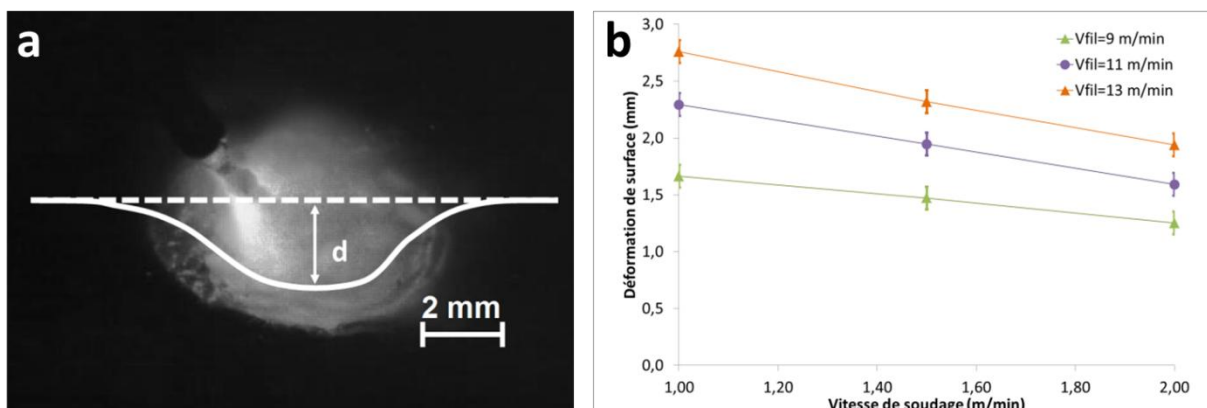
Mesures de la déformation de surface (a) et résultats obtenus en fonction de la vitesse de soudage (b) en soudage MAG
